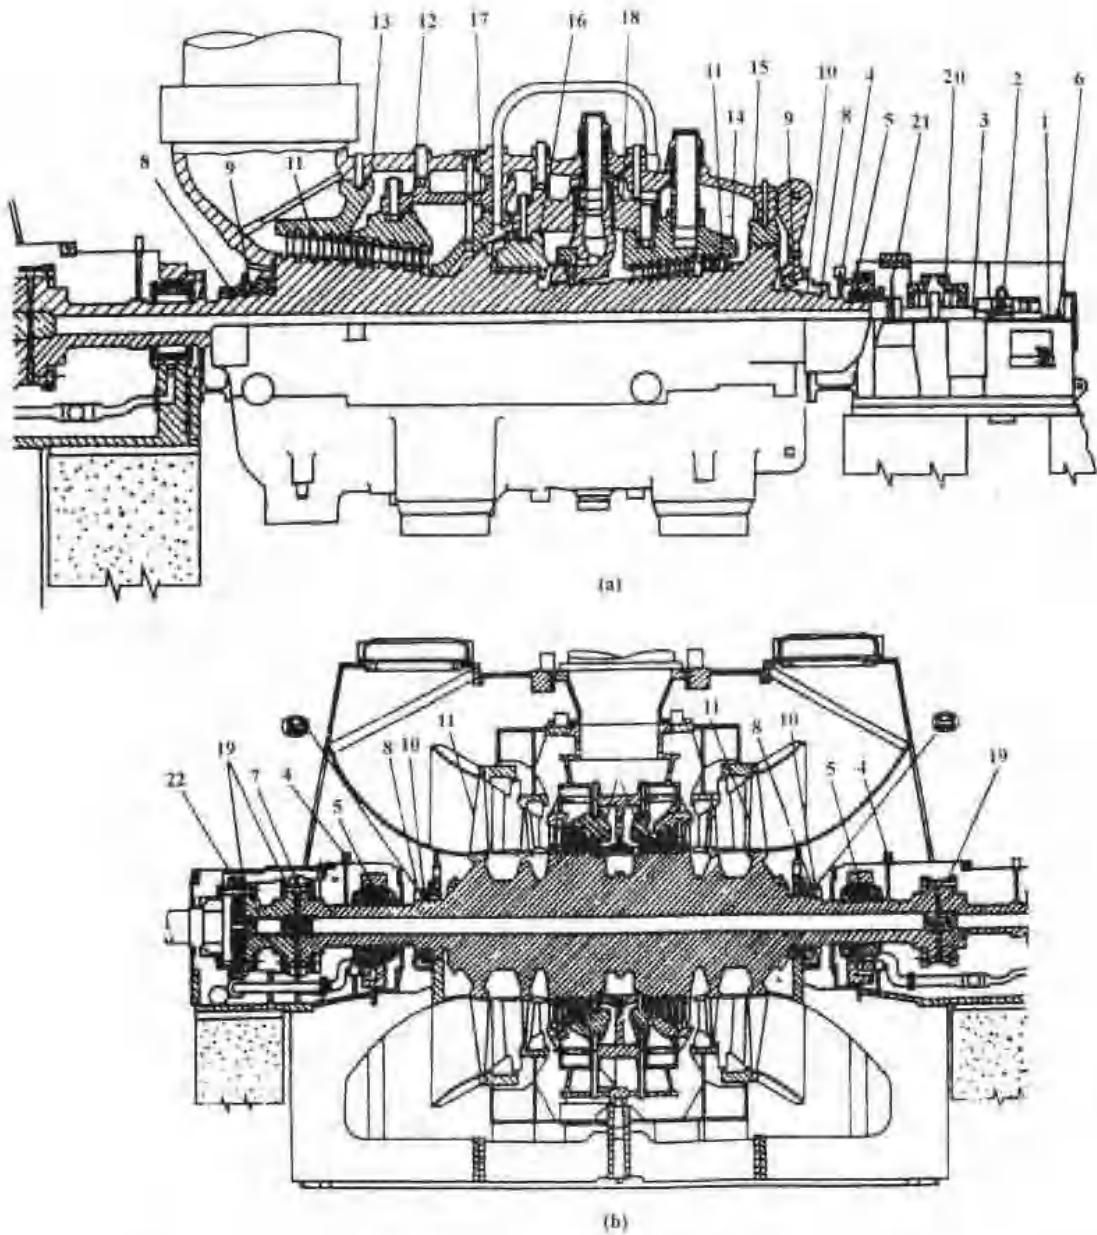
上海汽轮机厂生产的反动式 N300-16.7/538/538 型汽轮机纵剖面图
